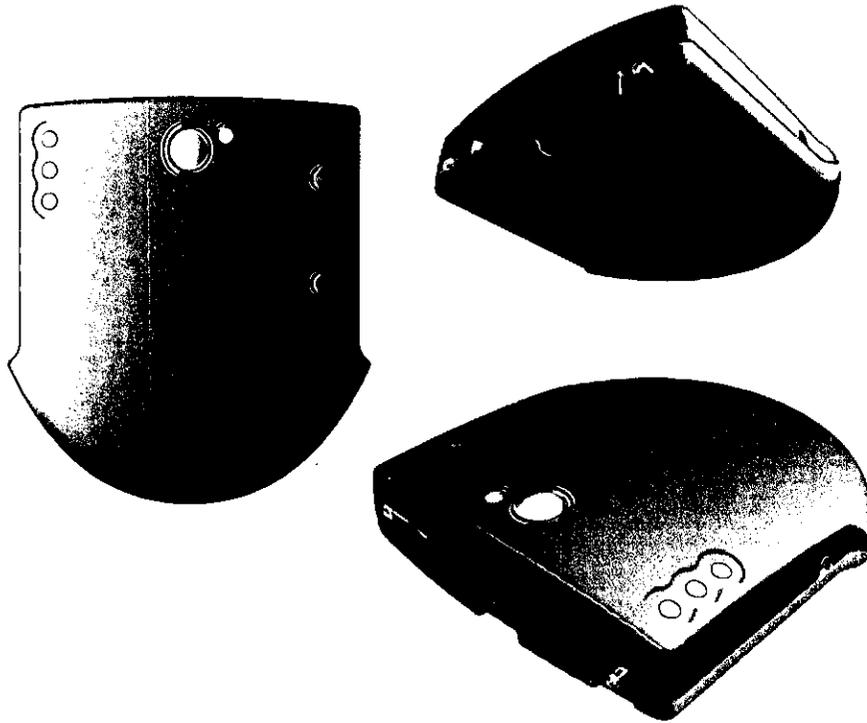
Vista Frontal (izquierda) e Isométricas (derecha) del Encapsulado.
